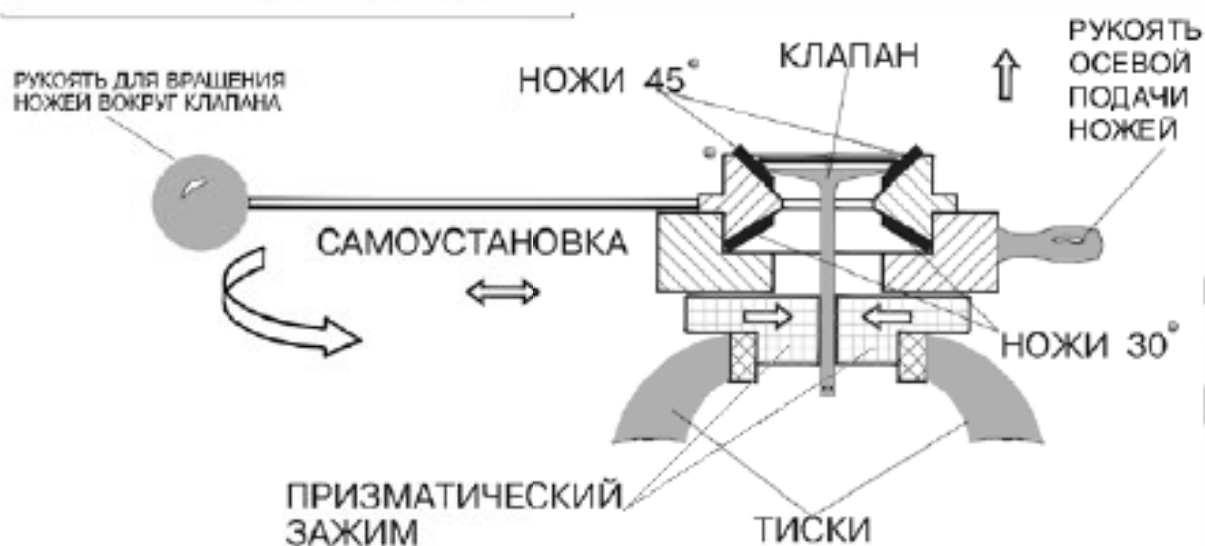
Ручний інструмент для ремонту клапанів.
